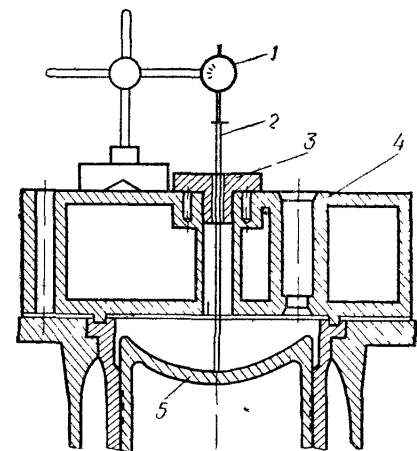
Определение в м. т. поршня с помощью линейного индикатора: 1 — индикатор, 2 — шток, 3 — направляющая втулка, 4 — цилиндрическая крышка, 5 — поршень
